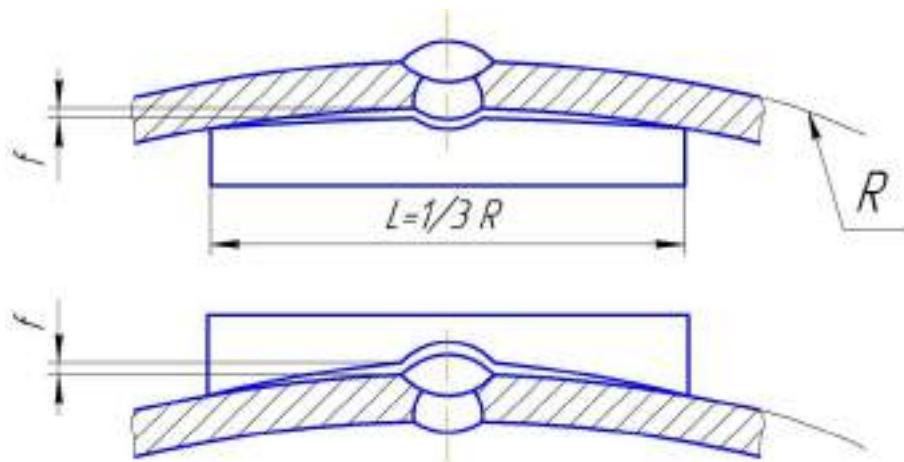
Схема замера угловатости сварного шва и отклонения формы детали от теоретической окружности в окколошовной зоне.
